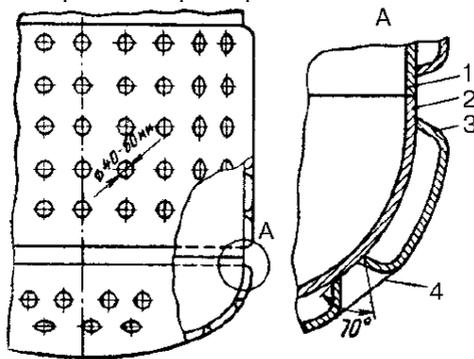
Рубашка реактора с «вмятинами»: 1 – корпус реактора; 2 – днище; 3 – рубашка; 4 – отбортованный край
